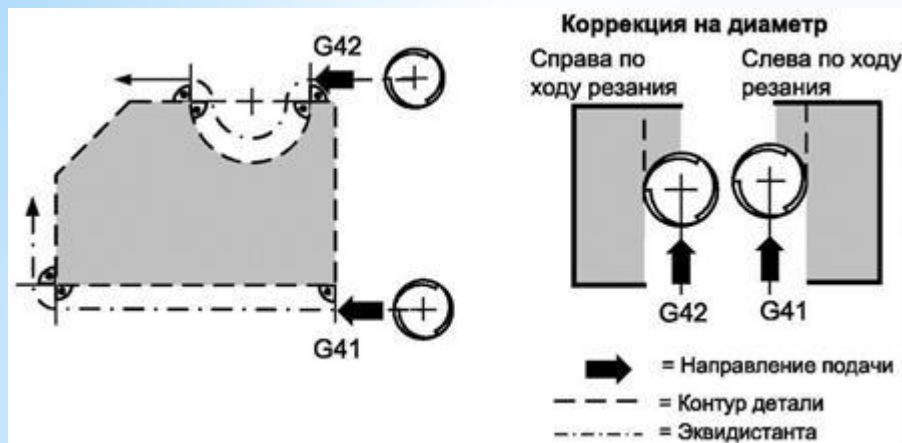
Принцип эквидистантной коррекции Рисунок 1 - Инструментальный комплекс
